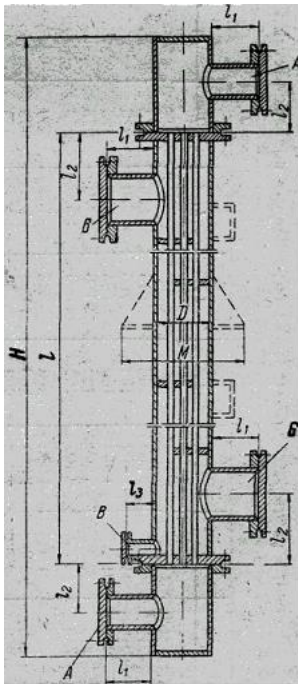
Одноходовой теплообменный аппарат типа ТН с диаметром корпуса 159 или 273мм, имеющий две камерные сварные крышки с плоскими доньшками
